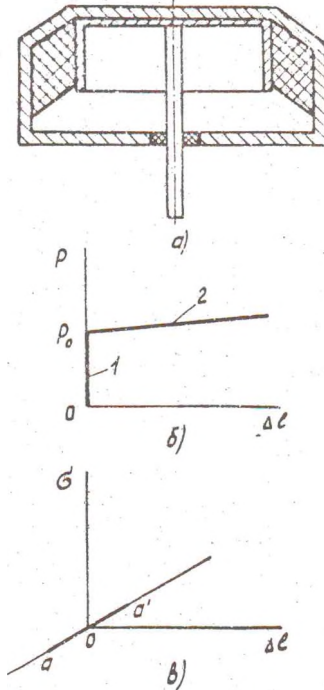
Конструкция резинометаллического амортизатора с предварительным поджатием резинового элемента.
